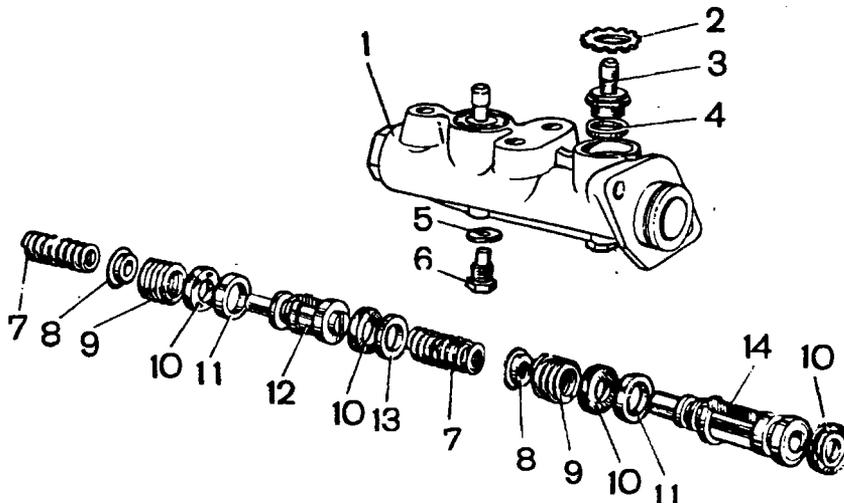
Детали главного цилиндра привода тормозов: 1 - корпус цилиндра; 2 - стопорная шайба; 3 - штуцер; 4 - уплотнительная прокладка; 5 - уплотнительная шайба; 6 - стопорный винт поршня; 7 - возвратные пружины поршней; 8 - чашка; 9 - прижимная пружина уплотнительного кольца; 10 - уплотнительное кольцо; 11 - распорное кольцо; 12 - поршень привода задних тормозов; 13 - шайба; 14 - поршень привода передних тормозов
